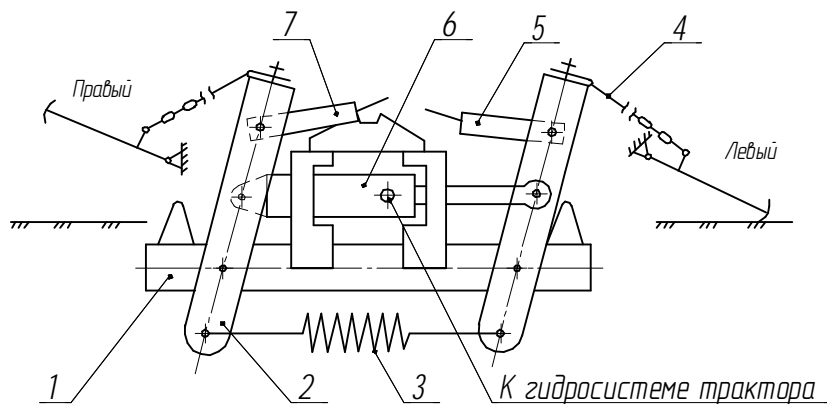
Схема механизма управления маркерами (вид спереди):
